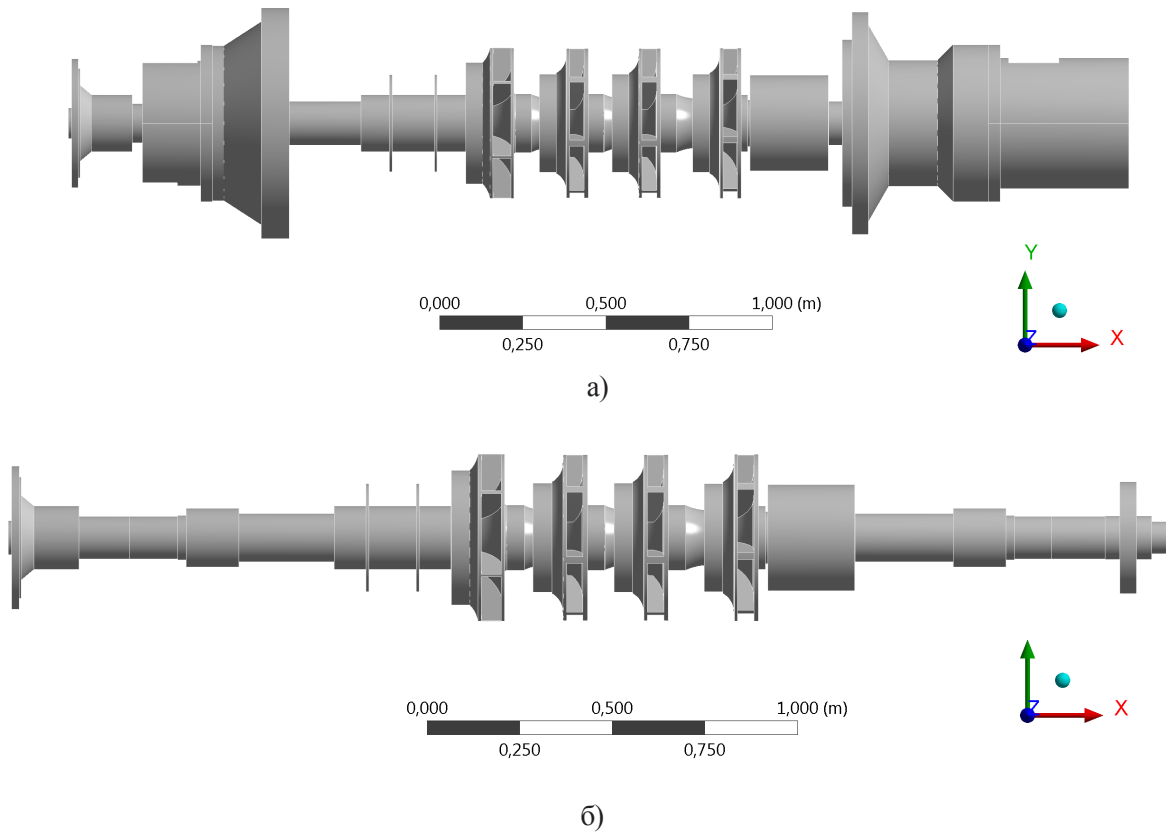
Геометрична модель ротора а) без урахування конструкції корпусу підшипникової опори б) з урахуванням конструкції корпусу підшипникової опори
